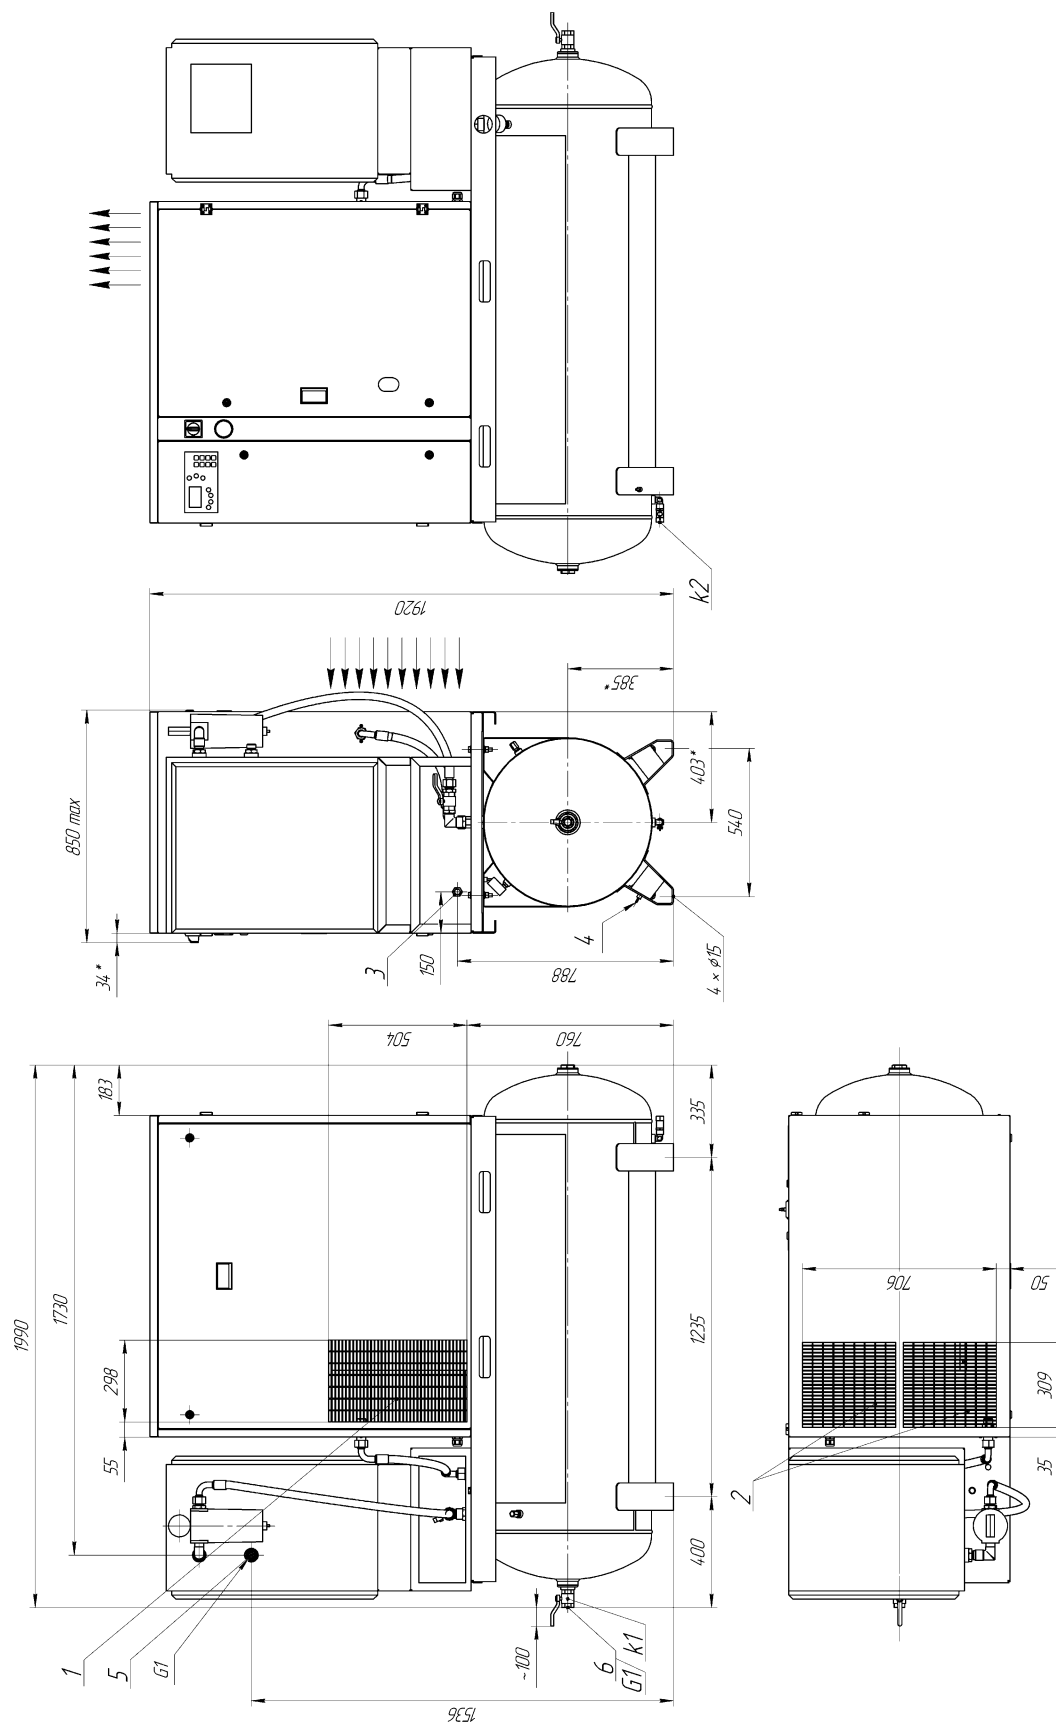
Присоединительные и установочные размеры компрессорных установок ВК25(30)-...-500(BC)
